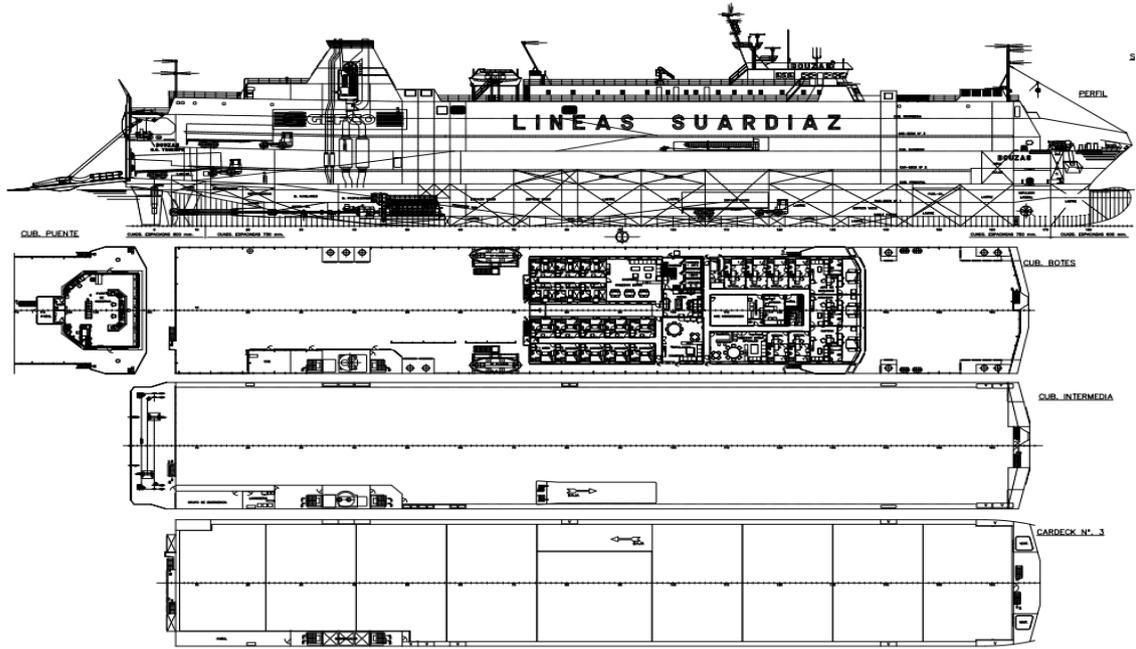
Planos Cubiertas Buque "L'Audace"
